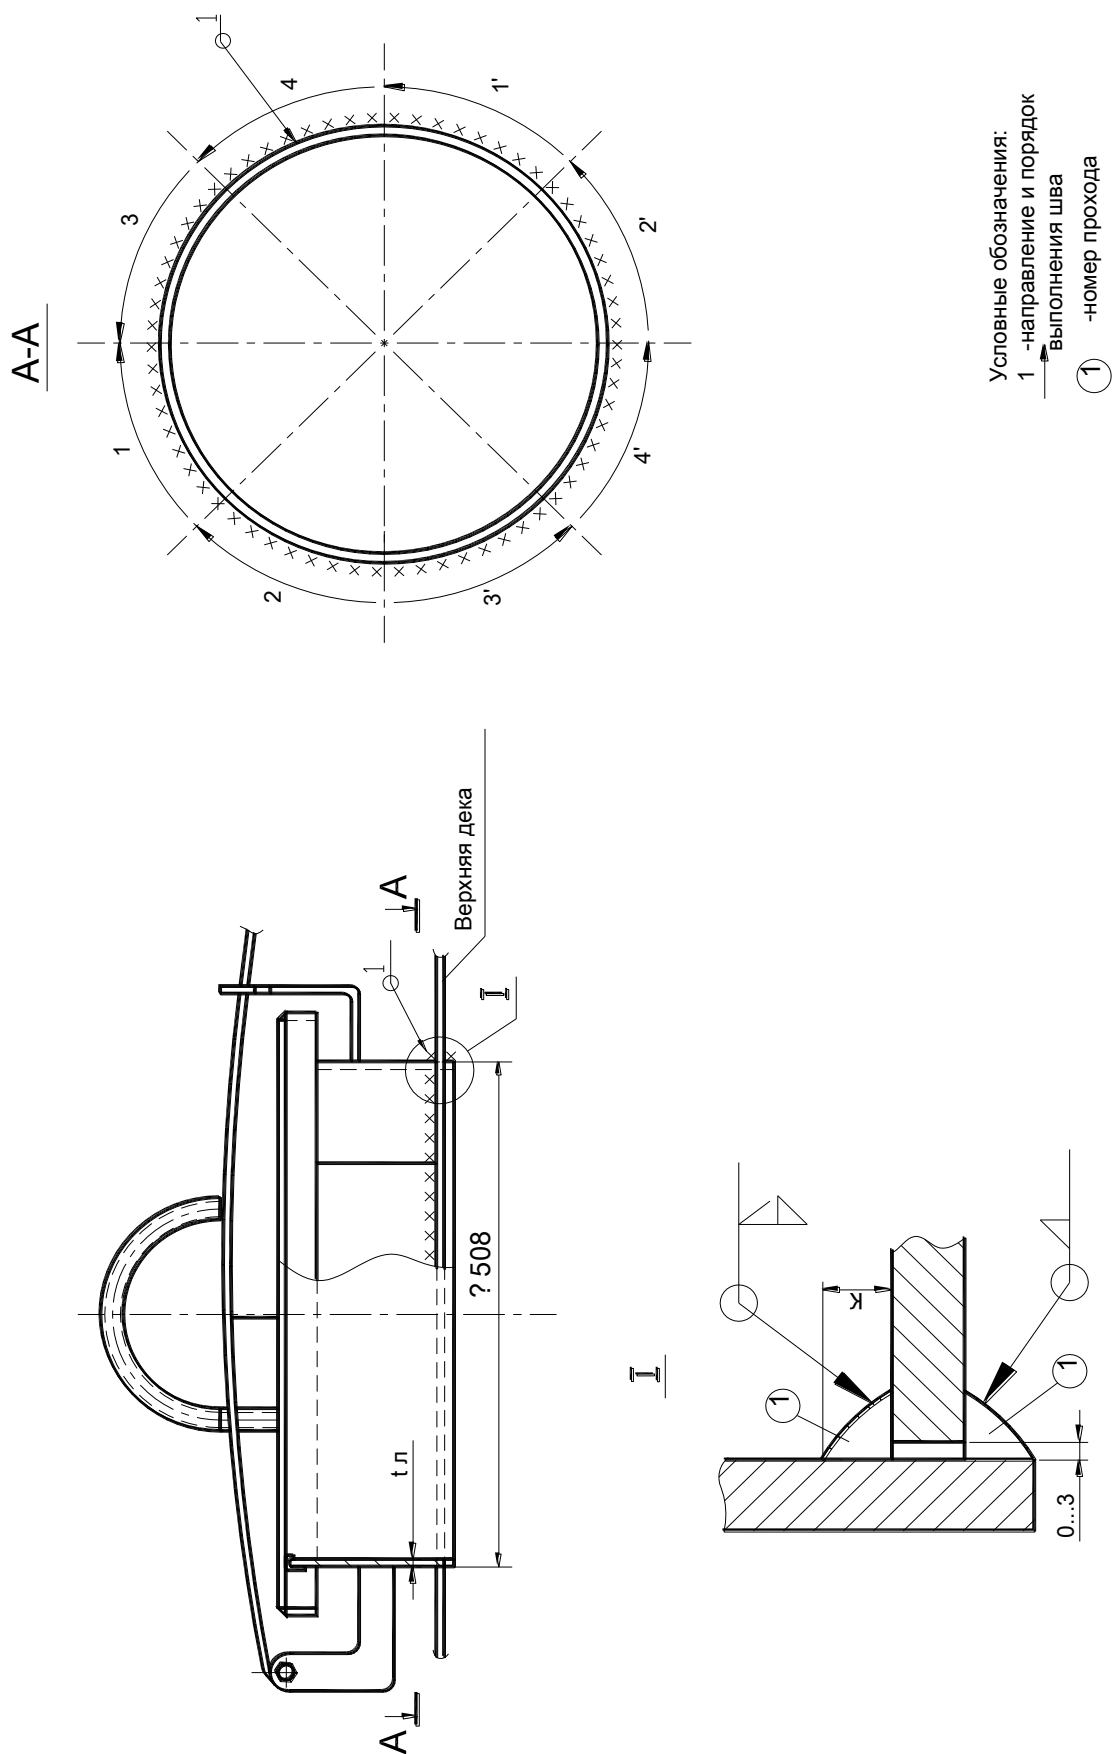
Схема сварки смотровых люков DN500 плавающей крыши
